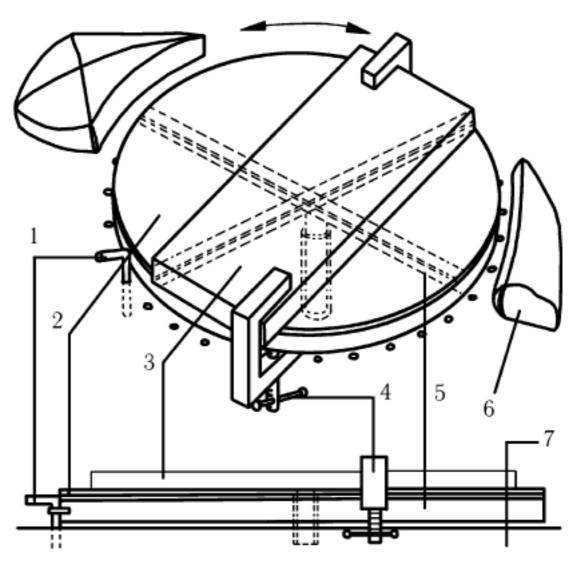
Устройство для вращения закрепленной заготовки: I — фиксатор; 2 — вращающийся диск; 3 — обрабатываемая заготовка; 4 — струбцина; 5 — ребра жесткости диска; 6 — подкладки; 7 — столешница
